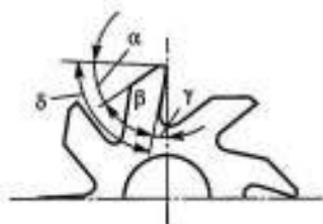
Геометрические параметры режущей части цилиндрической фрезы: γ — передний угол; α — задний угол; β — угол заострения; δ — угол резания
